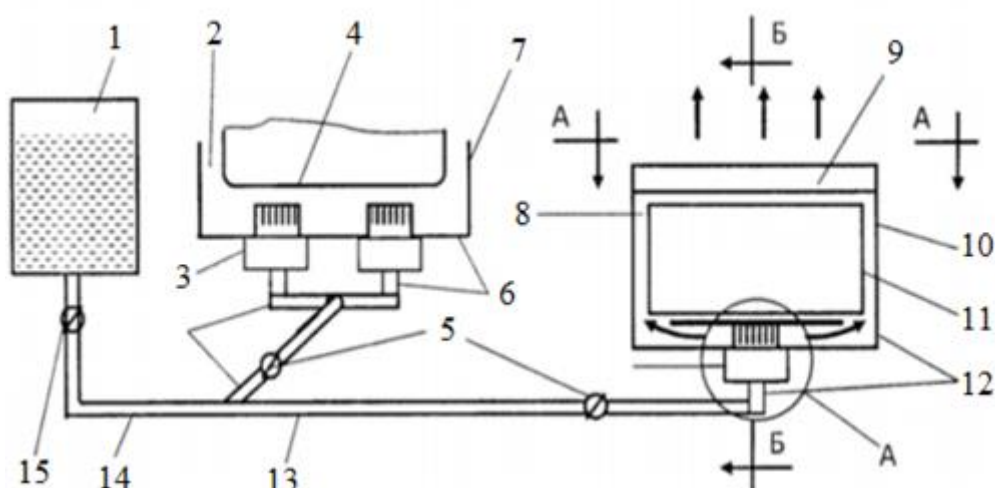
Схема устройства: 1- незамерзающая горючая жидкость; 2,8- газовый зазор; 3- патрубок; 4- днище картера; 5,15 - запорно– регулирующий клапан; 6- картер;7- тепловой поддон; 9- двухскатная крышка; 10-тепловая камера; 11- АКБ; 12- узел подвода;13,14- трубопровод.
